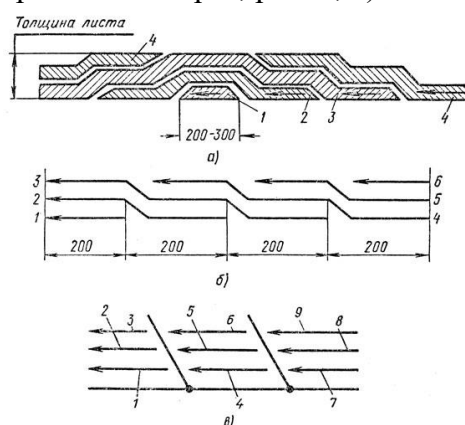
Методы сварки металла большой толщины: а - схема выполнения длинных многослойных швов 'горкой' (1-4 - последовательность наложения швов); б - схема сварки каскадом для выполнения длинных многослойных швов каскадом (1-6 - последовательность сварки); в - схема сварки блоками (1 - 9 - последовательность наложения слоев).
